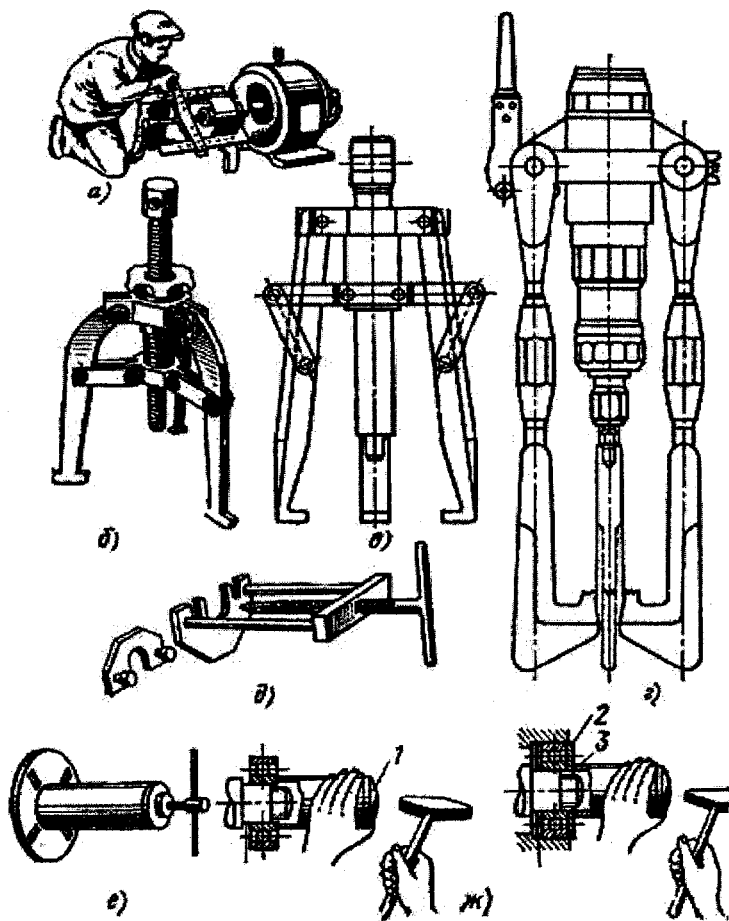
Снятие шкива, полумуфты, шестерни; снятие и насадка подшипников качения:
